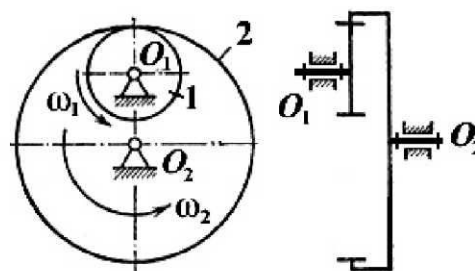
Зубчатая передача с внутренним зацеплением колес
